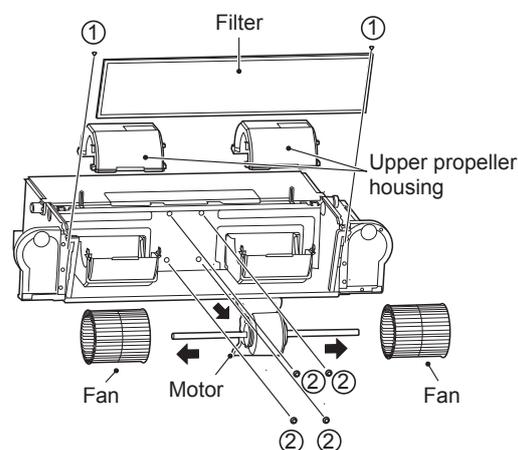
Desmontaje del filtro, la voluta superior y los tornillos del motor
